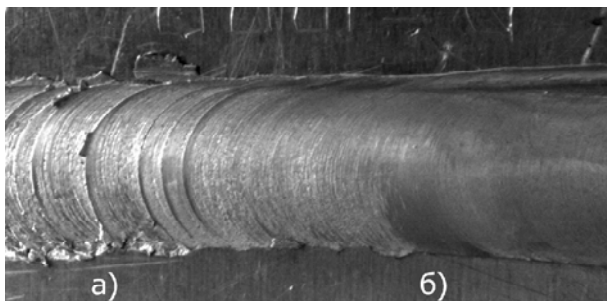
Зовнішній вигляд поверхні зварного шва залежно від умов роботи інструмента:
